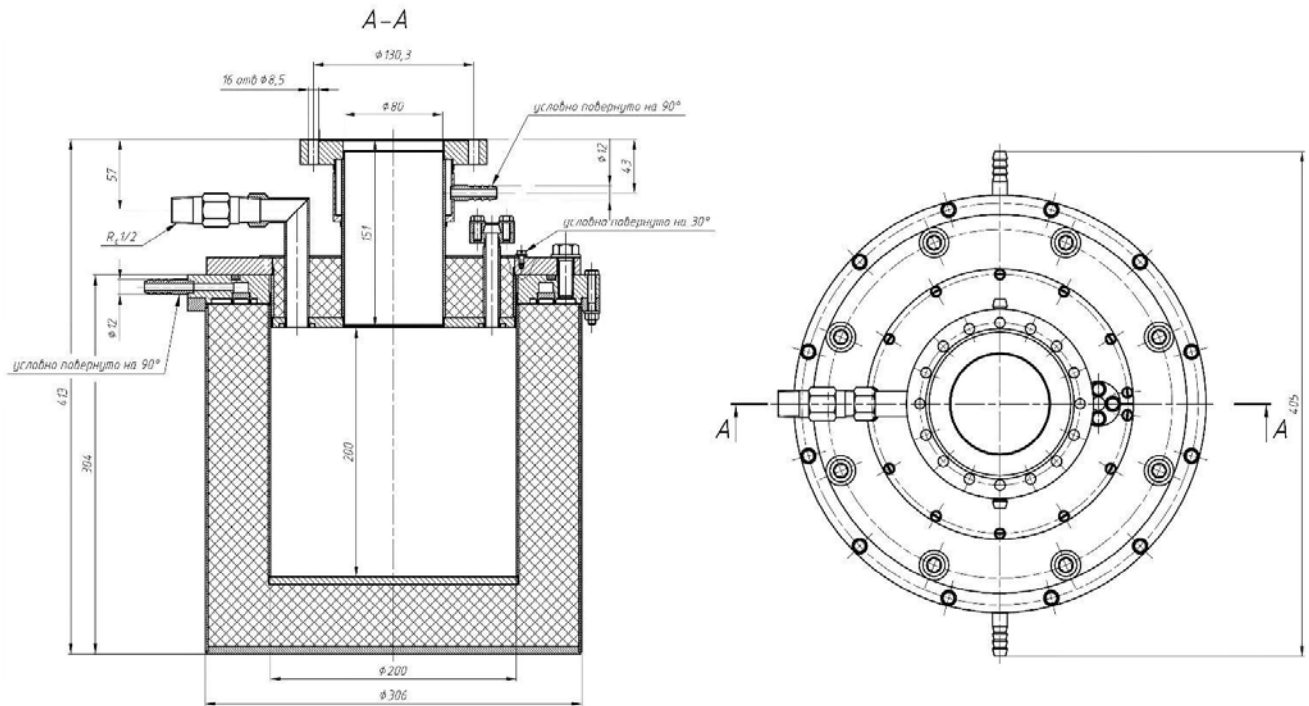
Сборочный чертеж сверхразмерного цилиндрического резонатора для реактора СВЧ - пиролиза «средней» загрузки (до 3 кг сырья)
